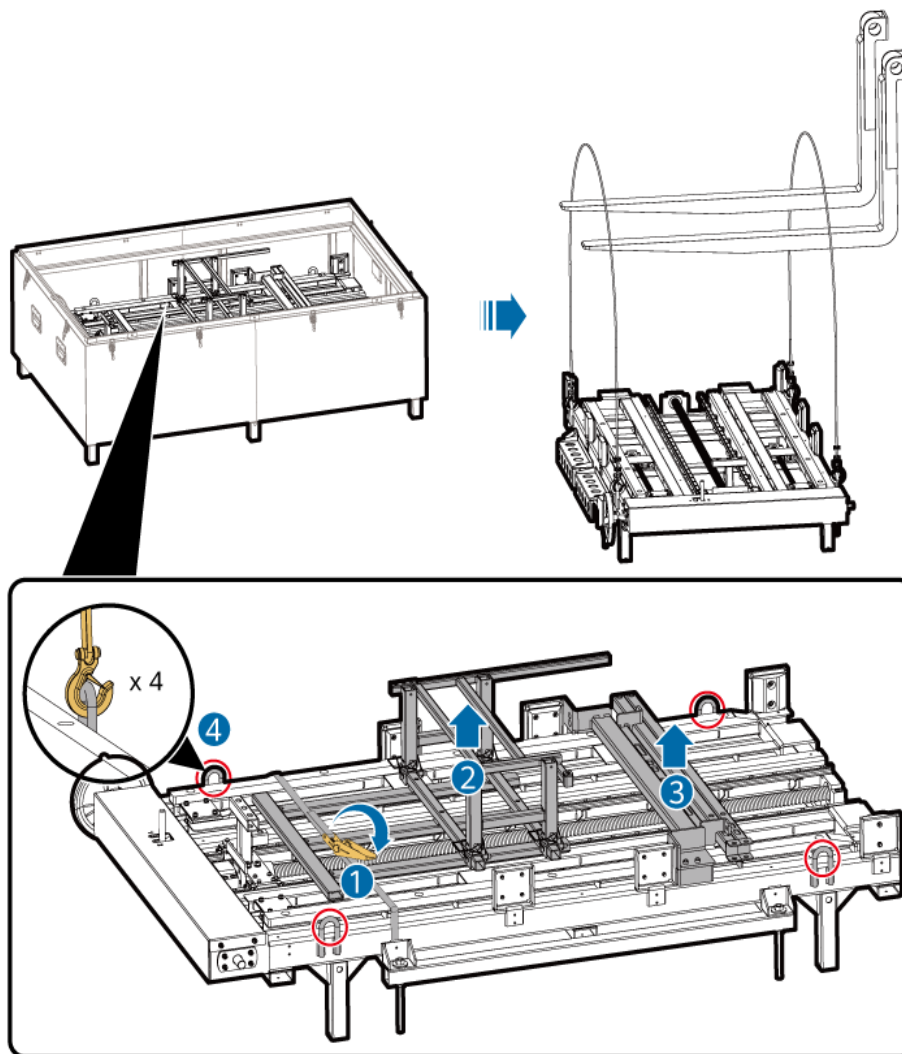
Disimballaggio dei dispositivi di fissaggio
